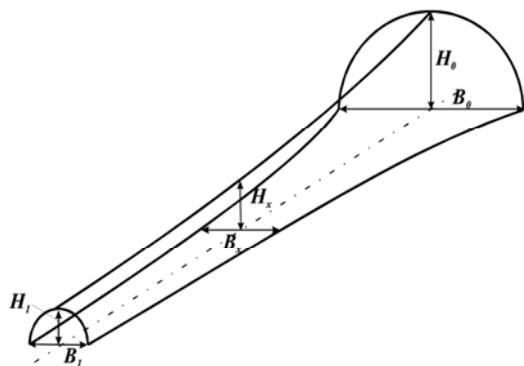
Существующий метод расчета формы рабочей поверхности калибров для станков ХПТ
